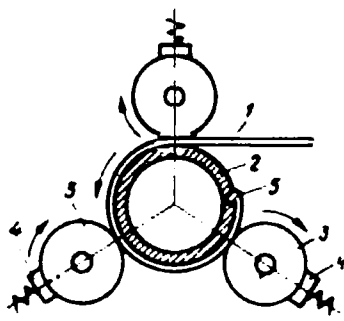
Схема свивания заготовки на трубонавивочном станке:
